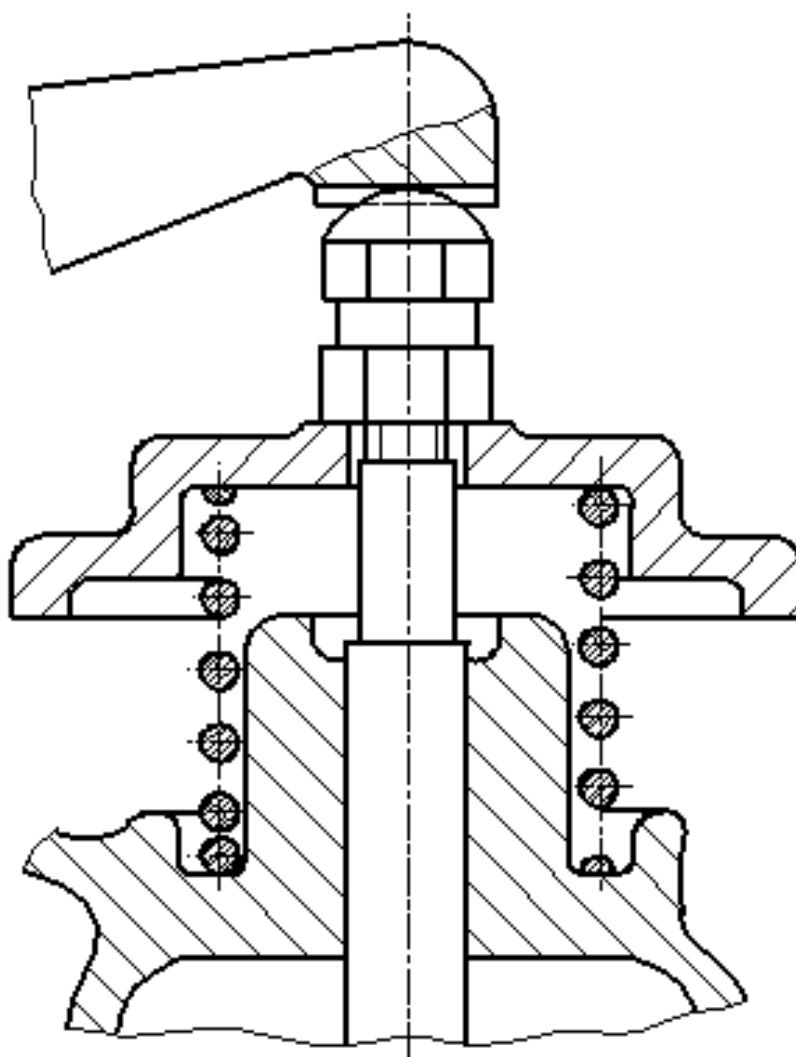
Пример изображения винтовой пружины на сборочном чертеже
